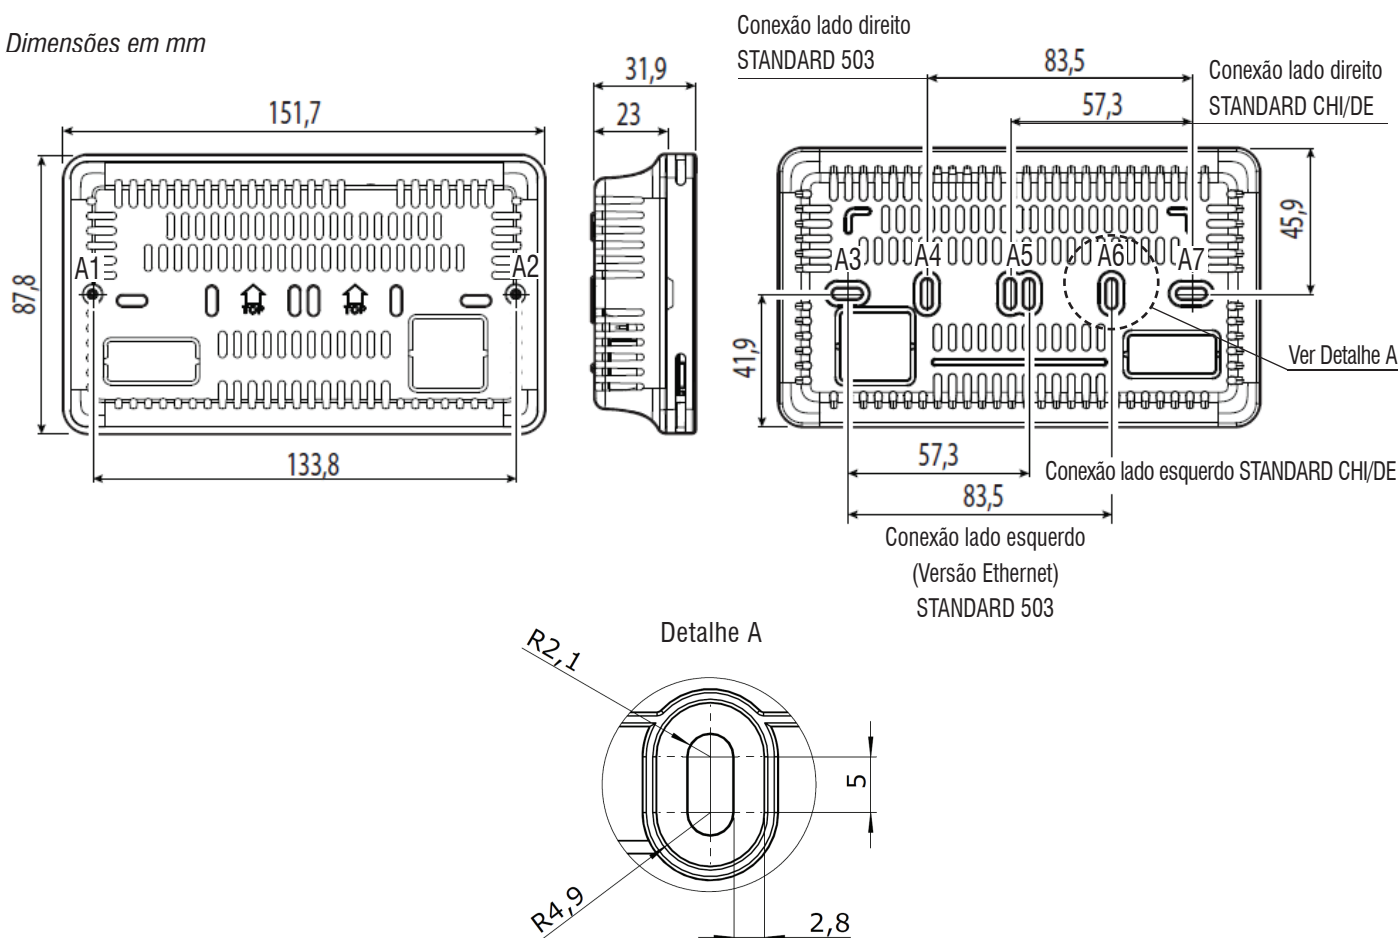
FIXAÇÃO DA WALL BOX NA PAREDE
